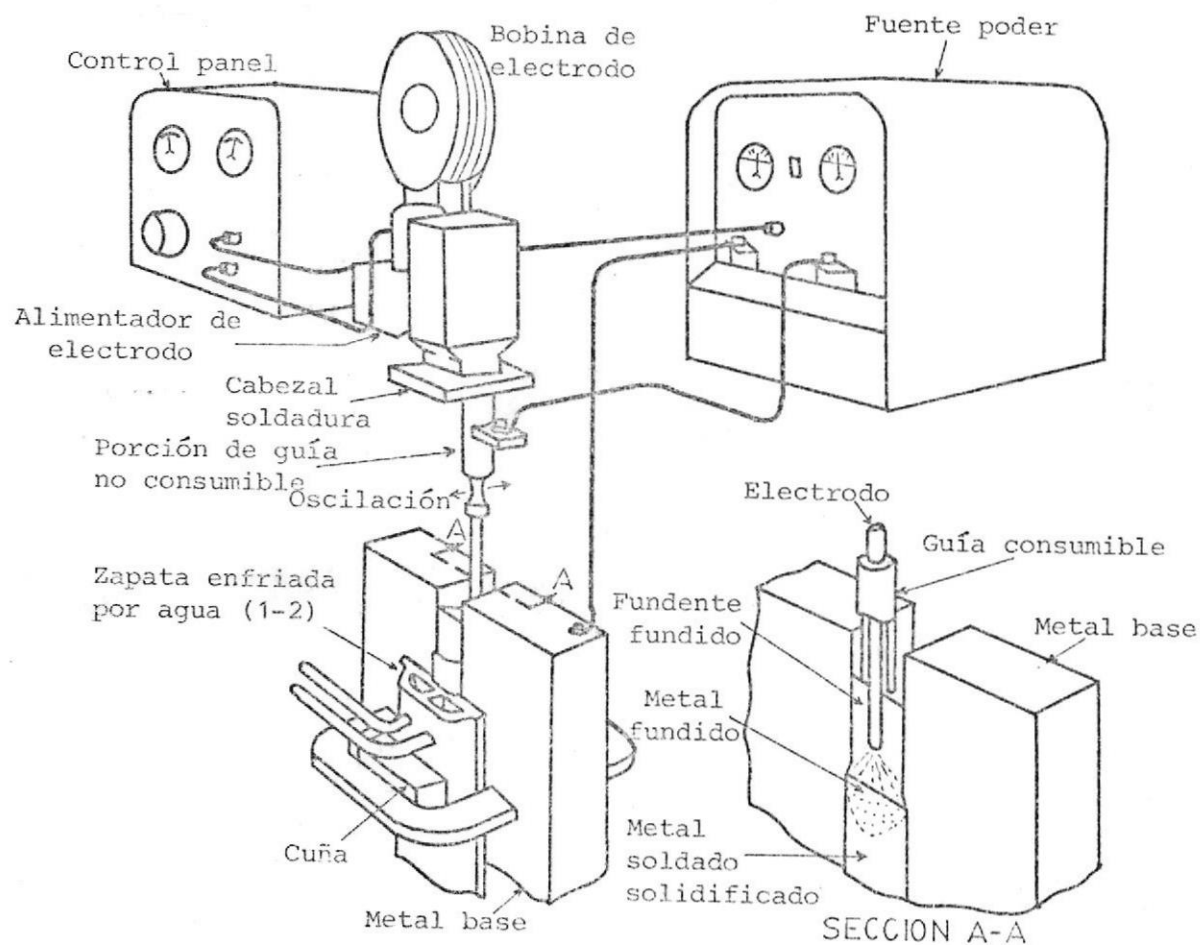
Componentes principales de un equipo para soldadura por electroescoria usando guía consumible (Ref. 1).
